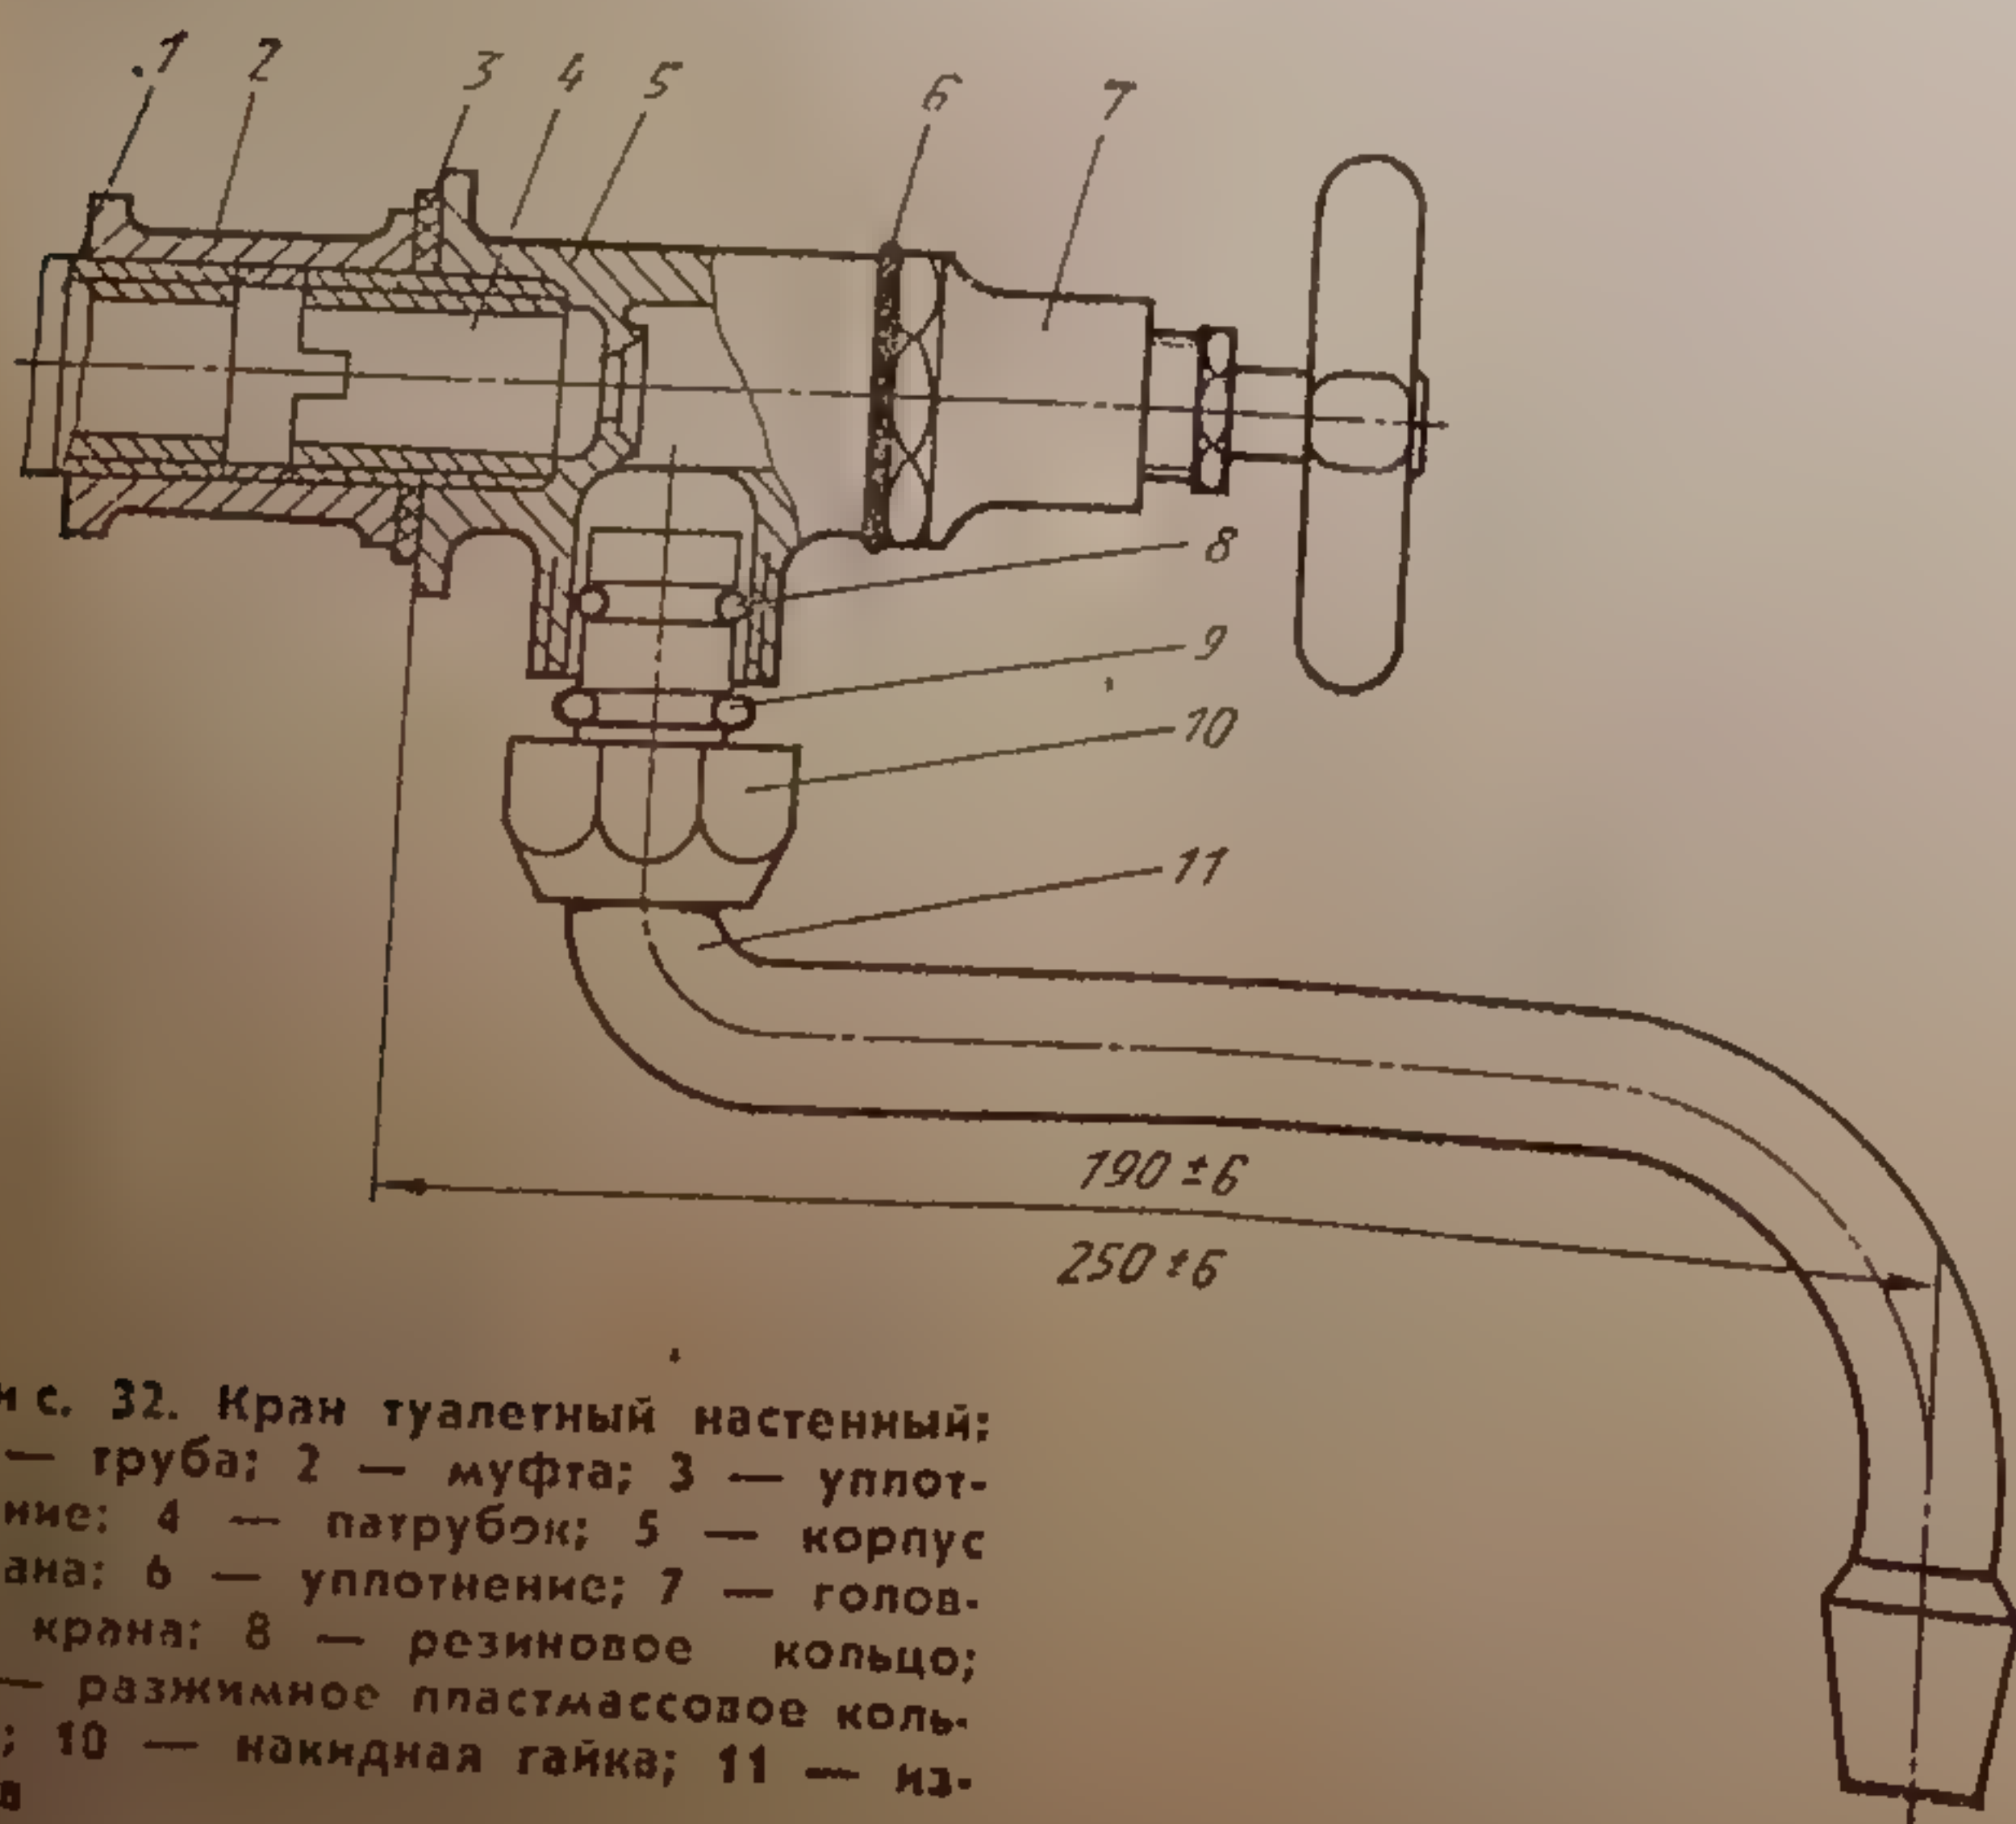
Кран туалетный настенный: 1 — труба; 2 — муфта; 3 — уплотнение; 4 — патрубок; 5 — корпус крана; 6 — уплотнение; 7 — головка крана; 8 — резиновое кольцо; 9 — разжимное пластмассовое кольцо; 10 — накидная гайка; 11 — излив
